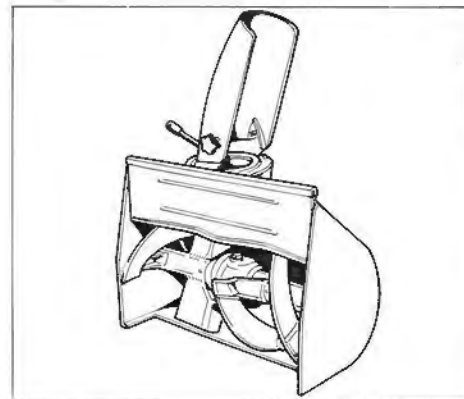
Spazzaneve - Schneefräse - Barrenieve
